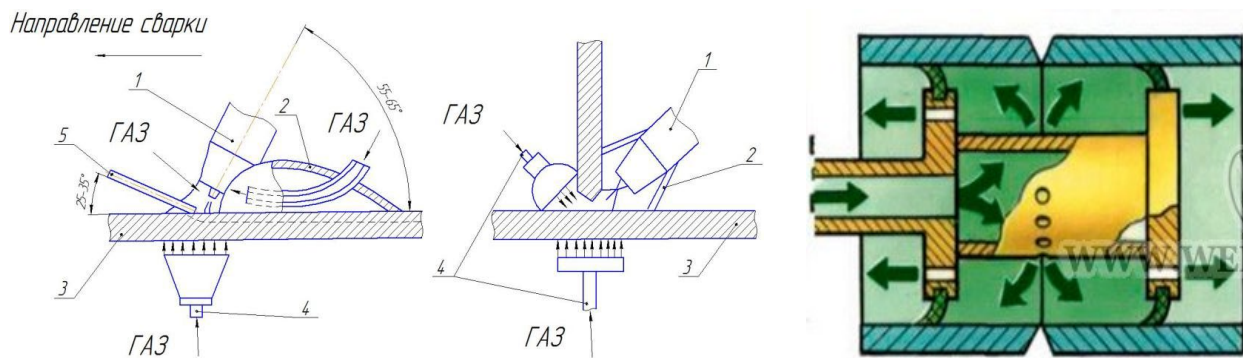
Схеми захисту зворотнього боку (кореня) шва при зварюванні. 1 – пальник; 2 – камера-насадка; 3 – виріб; 4 – поддув; 5 – присадний дріт.
